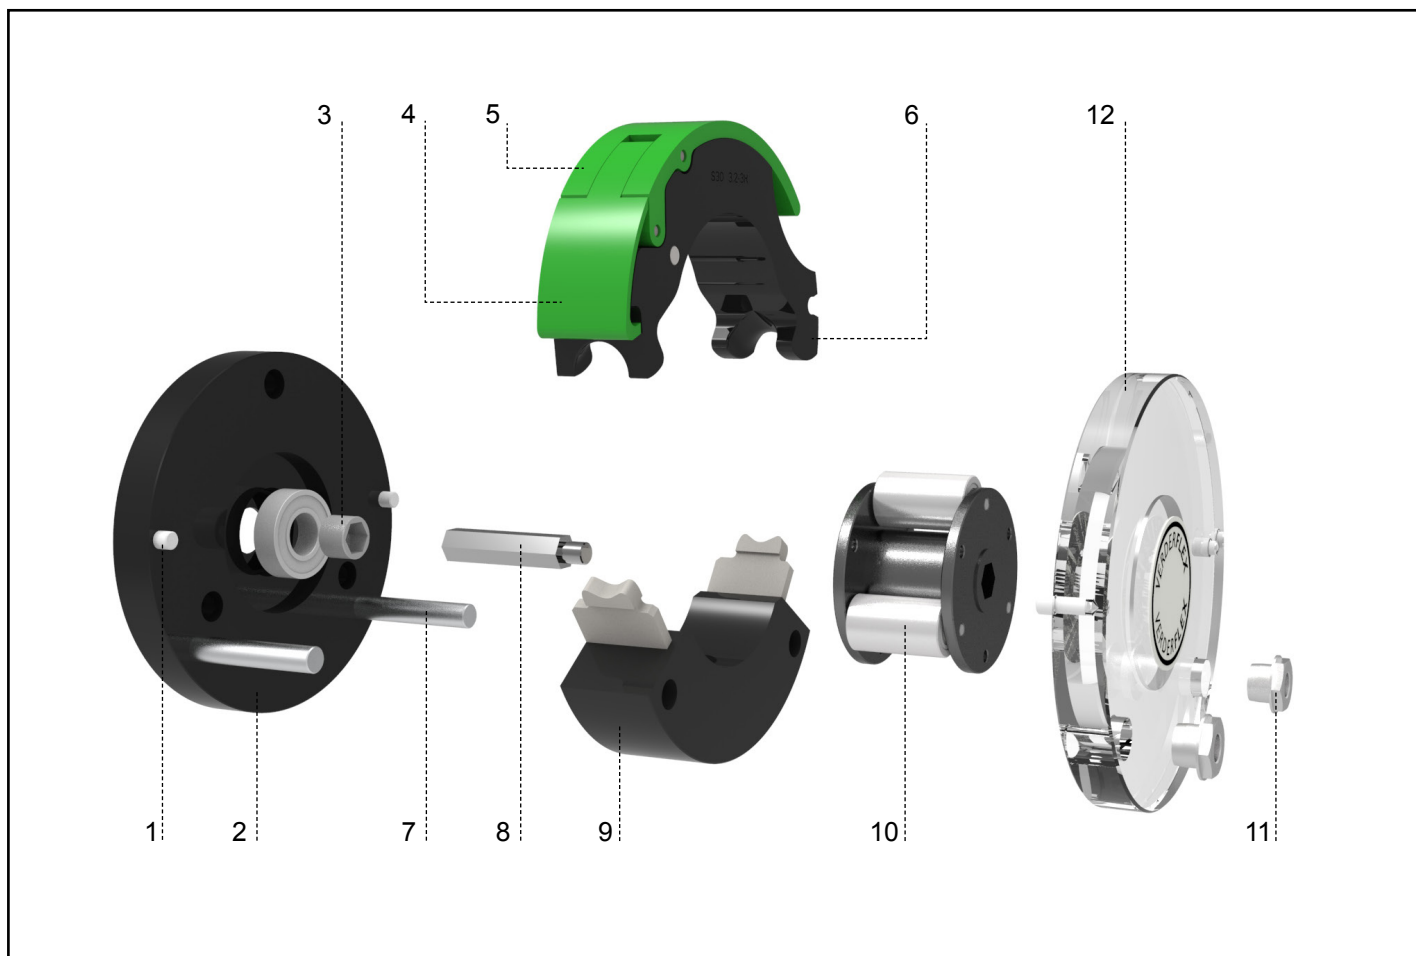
Explosionsansicht des Rapide S Pumpenkopfes
